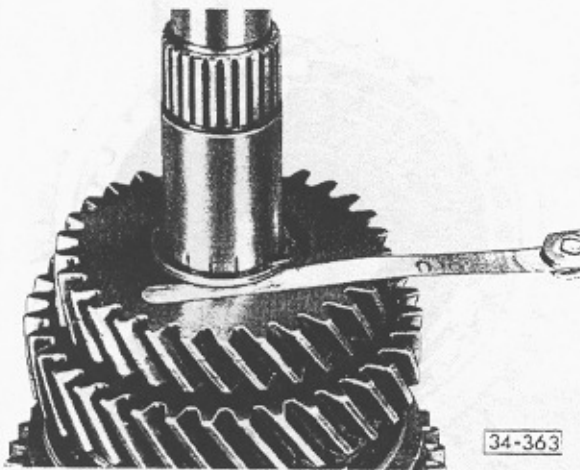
Axialspiel des Zahnrades für 3. Gang einstellen
